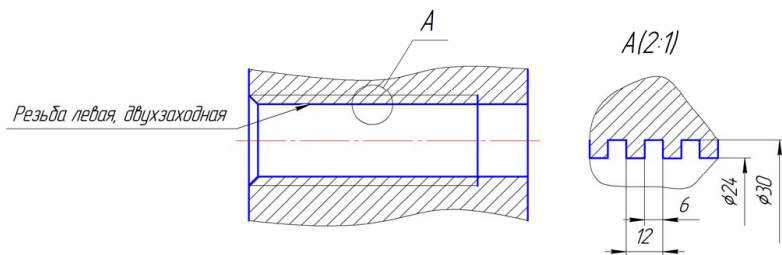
Изображение внутренней прямоугольной резьбы на чертеже
